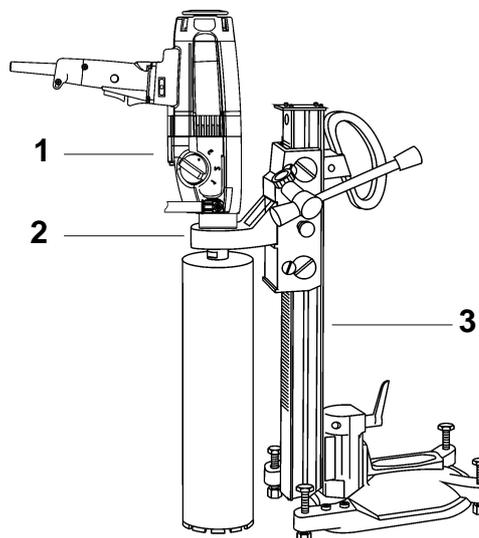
Freihandbohrmaschine am Bohrständler
